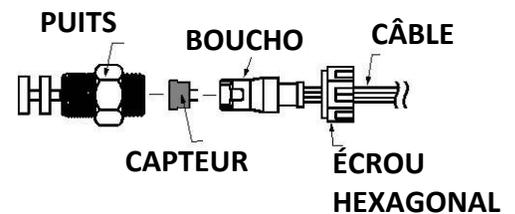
Vue éclatée d'un ensemble de thermostat étanche aux intempéries montrant la pièce de remplacement du capteur.
